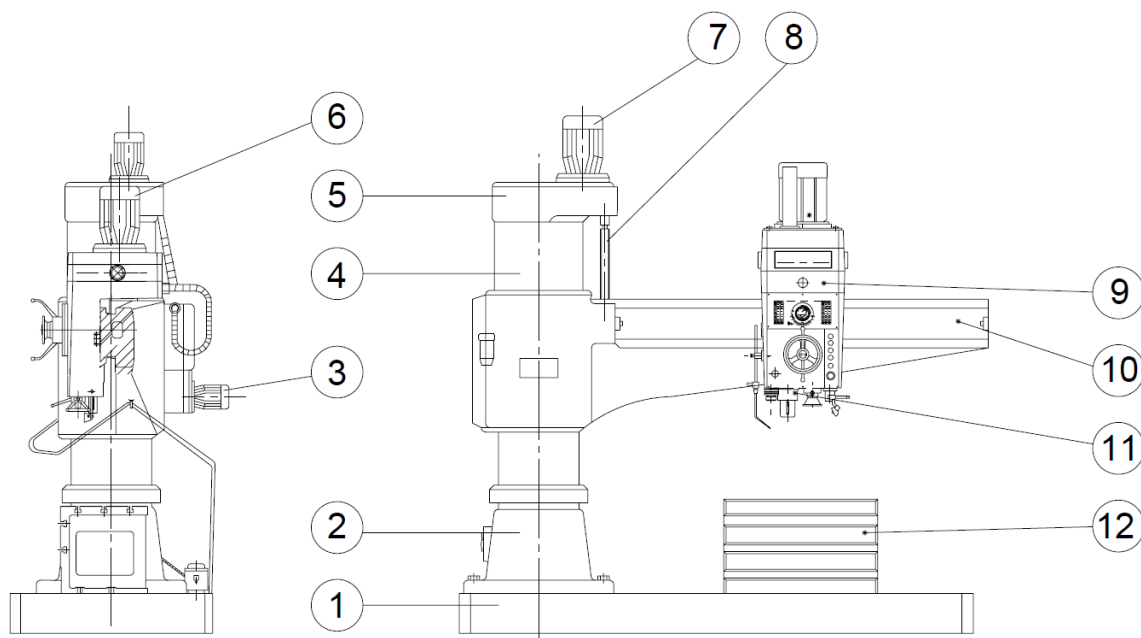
Радиально-сверлильный станок: 1 основание; 2 тумба; э/д насоса гидравлик; 4 колонна; 5 резервуар подъема опускания руки и зажима колонны; 6 э/д шпинделя; 7 э/д подъема/опускания руки; 8 винт подъема/опускания руки; 9 Шпиндельная бабка; 10 рука
